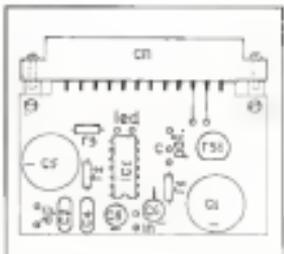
Piano di assemblaggio dei componenti sul circuito stampato
